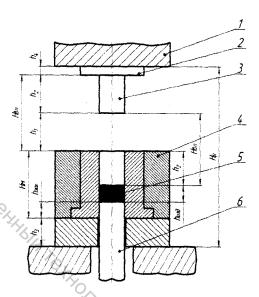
Схема для расчета технологических параметров прессового оборудования: 1 - ползун; 2 — плита; 3 — пуансон; 4 — пресс-форма; 5 - прессовка; 6 = выталкиватель
